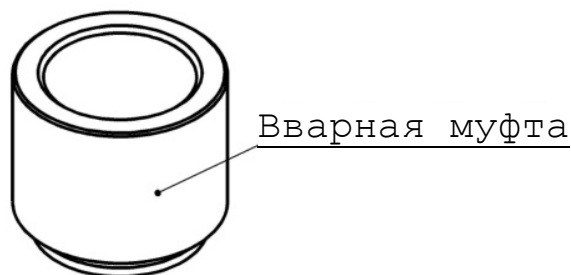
Вварная монтажная деталь (вварная муфта)
